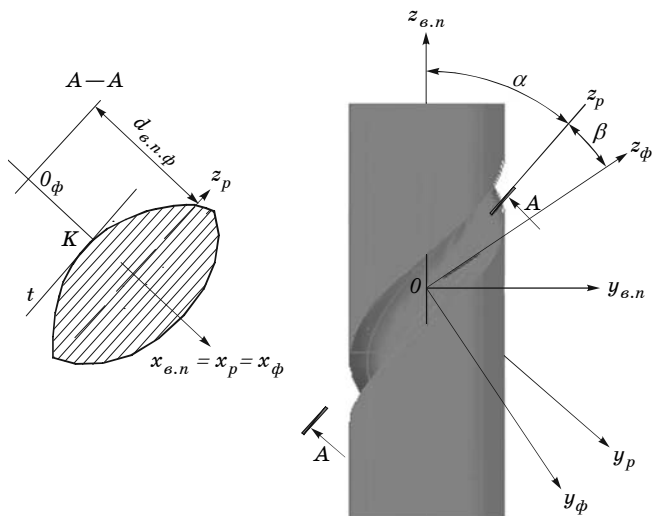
Сечение модели тела детали с винтовой поверхностью плоскостью, параллельной образующей цилиндрической поверхности инструментальной рейки
